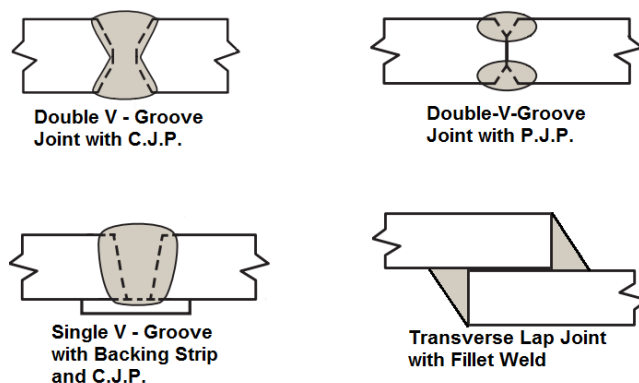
Tipos de uniones soldadas para estanques. [3]
